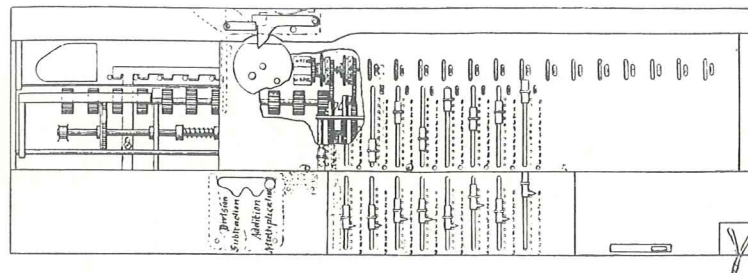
Draufsicht auf die elektrische Rechenmaschine von Alex. Rechnitzer mit teilweise entferntem Deckblech
